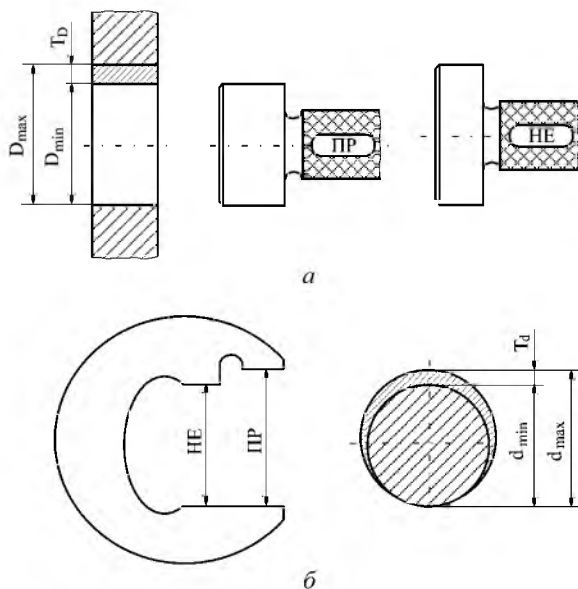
Схемы контроля гладкими предельными калибрами отверстия (а) и вала (б)
